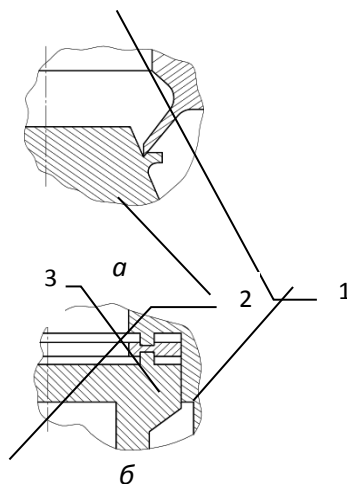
Конструкція метал-металевого затвора з пластичною деформацією елементів: 1 — золотник, 2 — сідло, 3 — пластина для пластичної деформації
